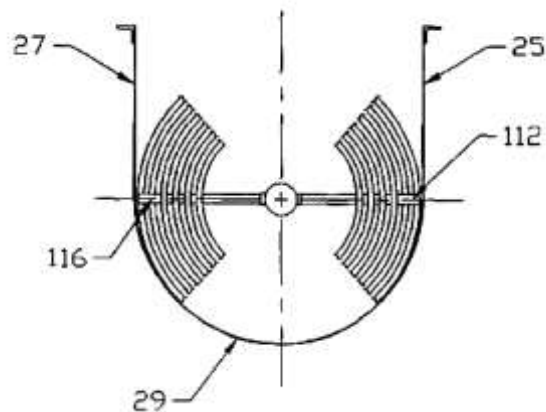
Secțiune rotor cu panglici elicoidale [2]
